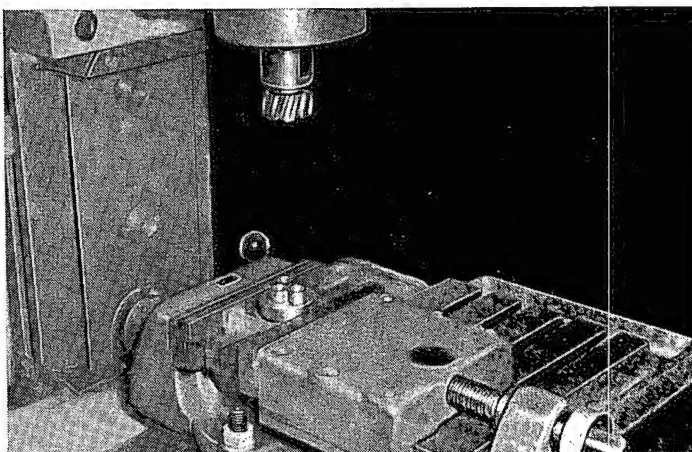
Тиски с длинным упором для закрепления пакета плоских деталей.
